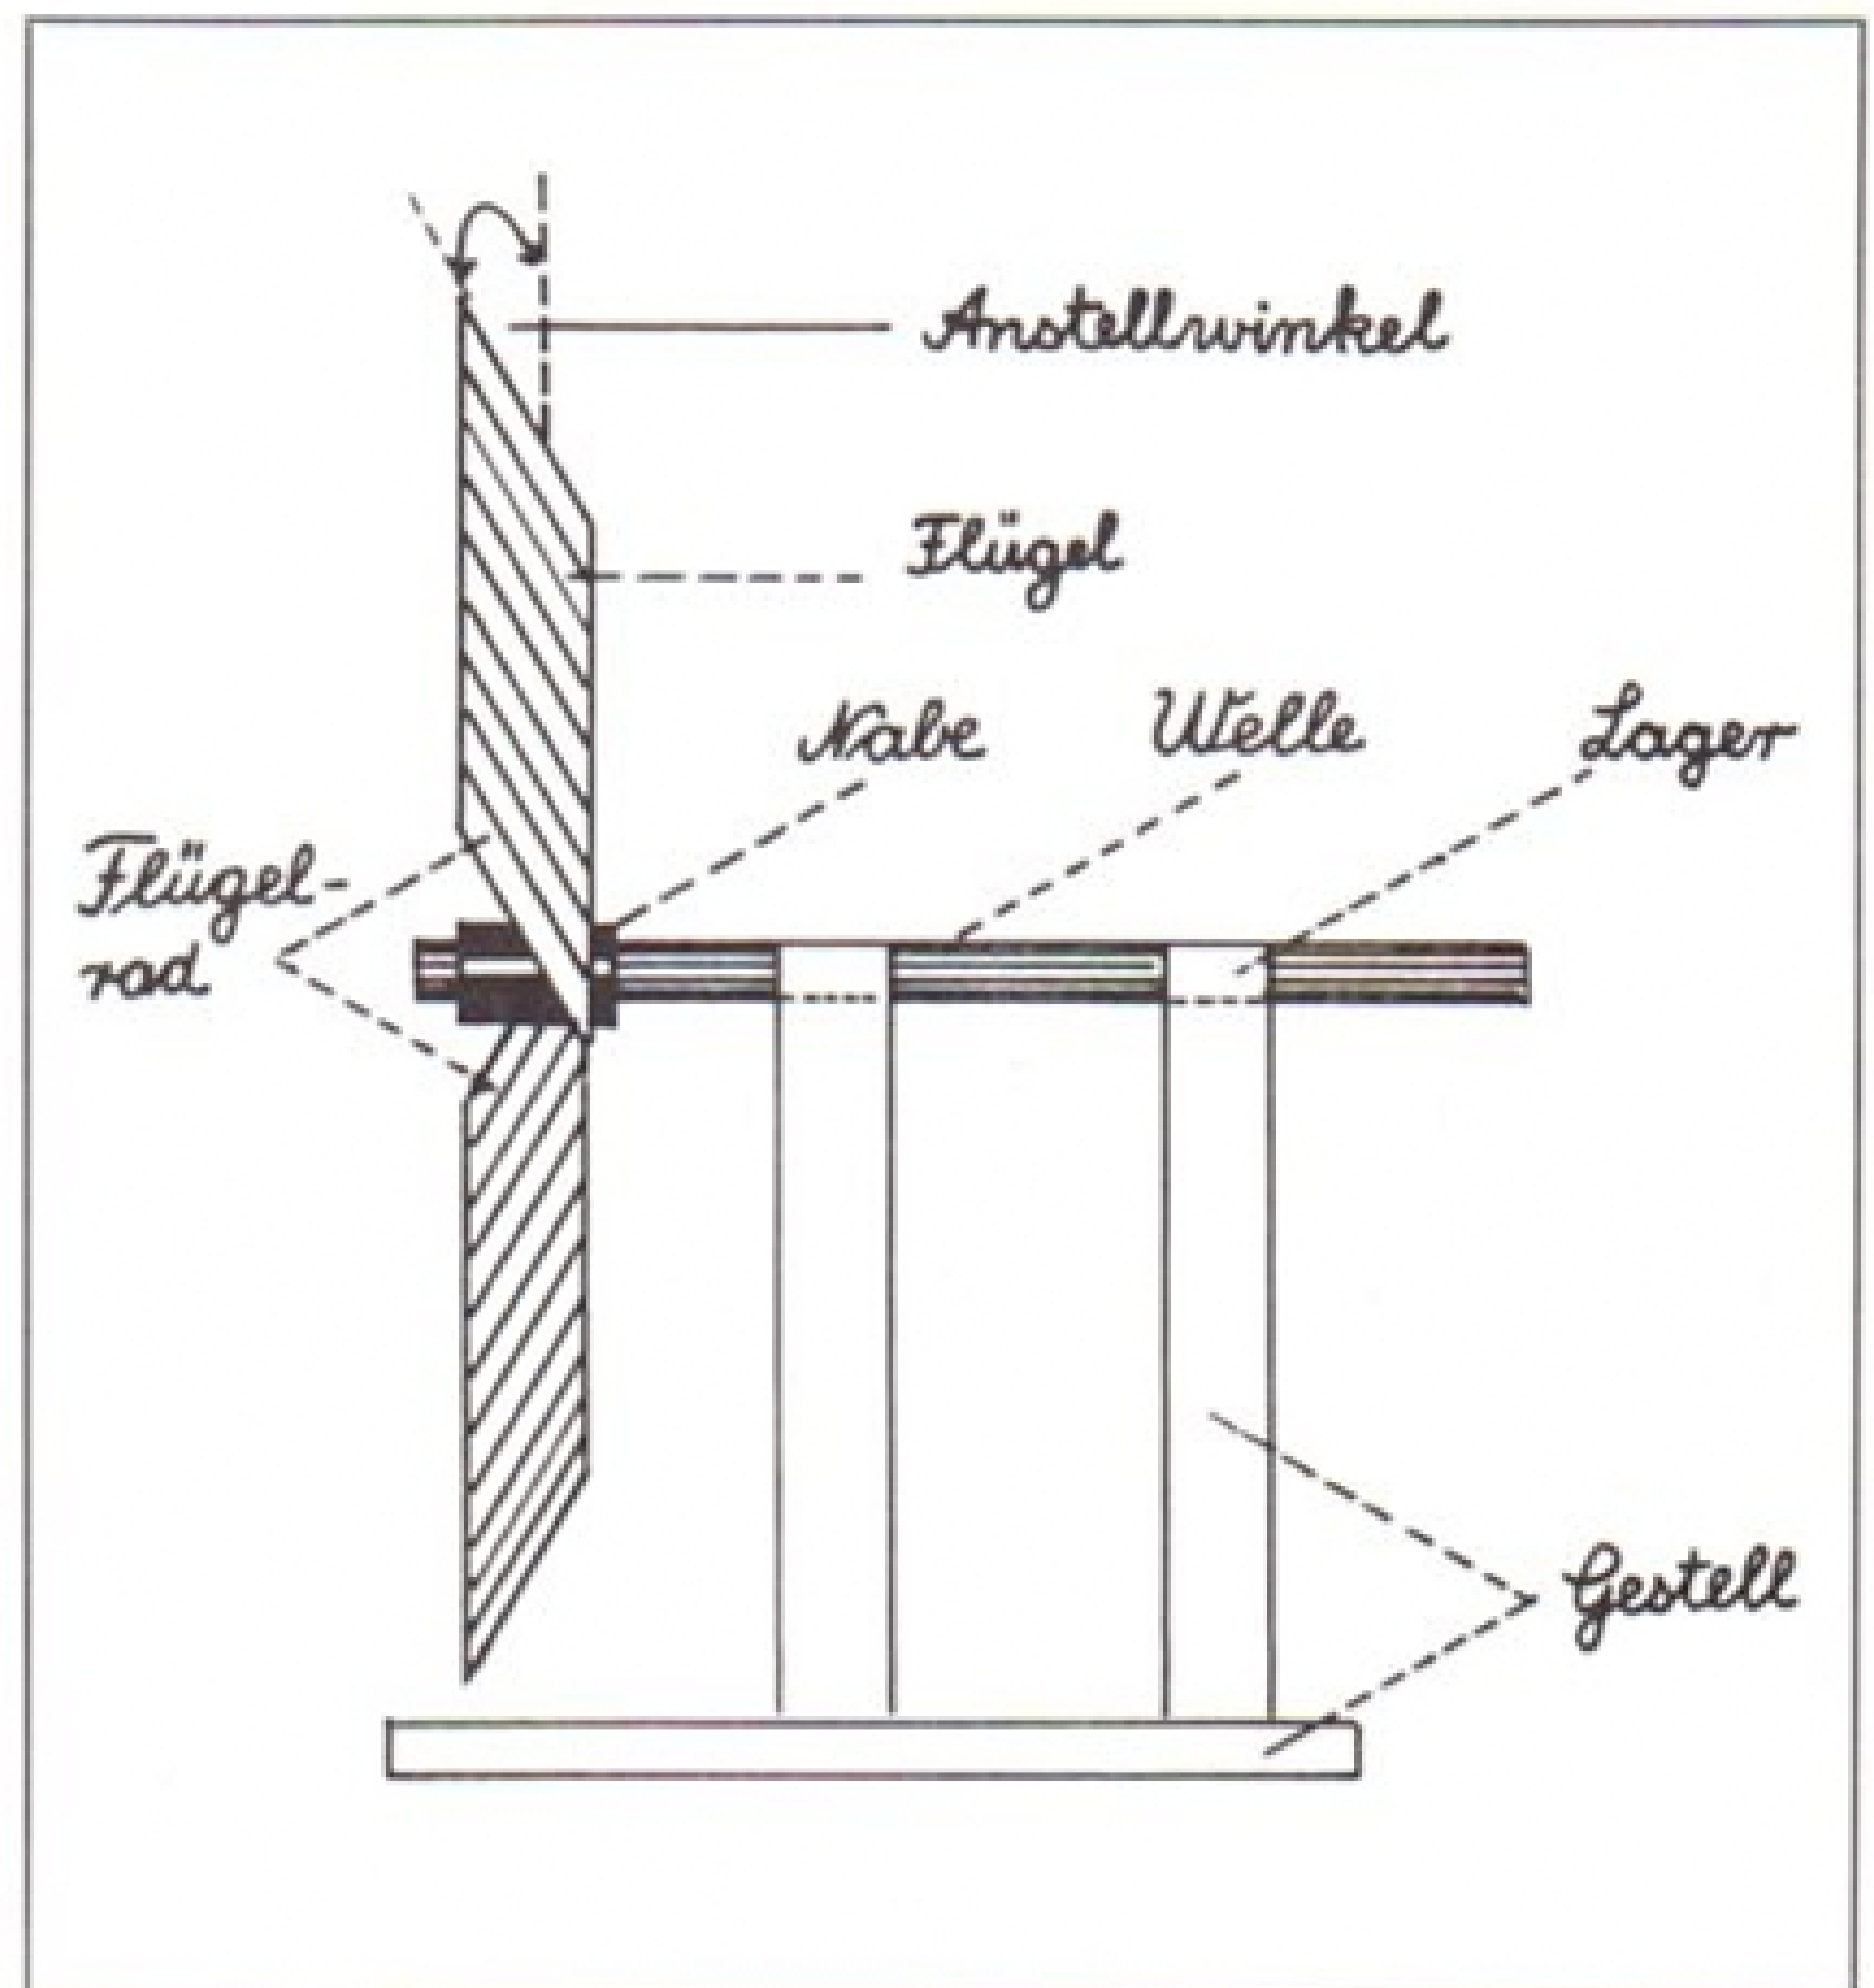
Anhand dieser Skizze können wichtige Begriffe geklärt werden.
